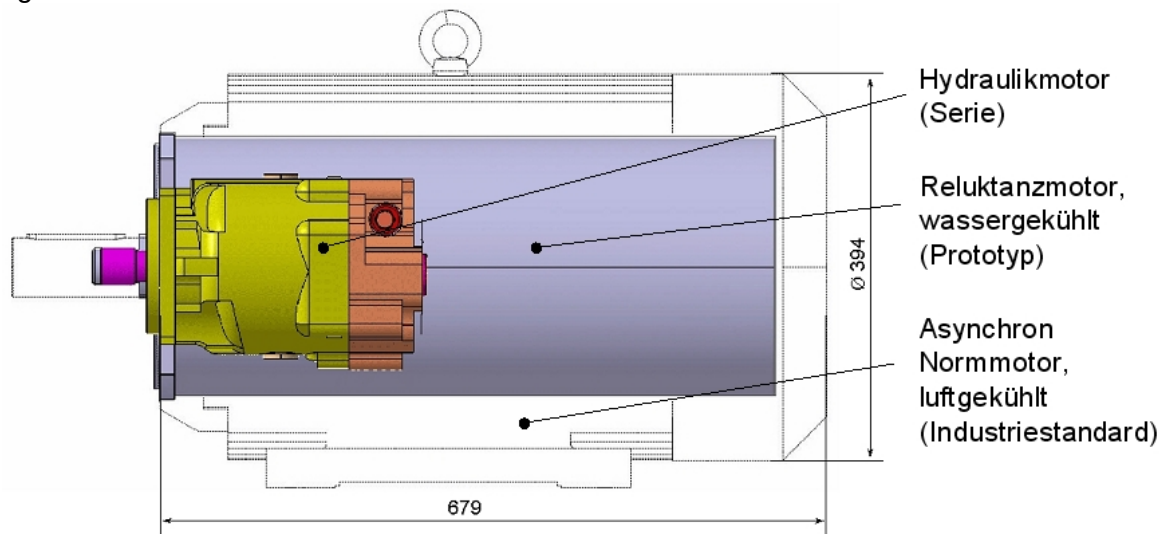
Dimension des hydraulischen Einzugsmotor und elektrischer Alternativen
